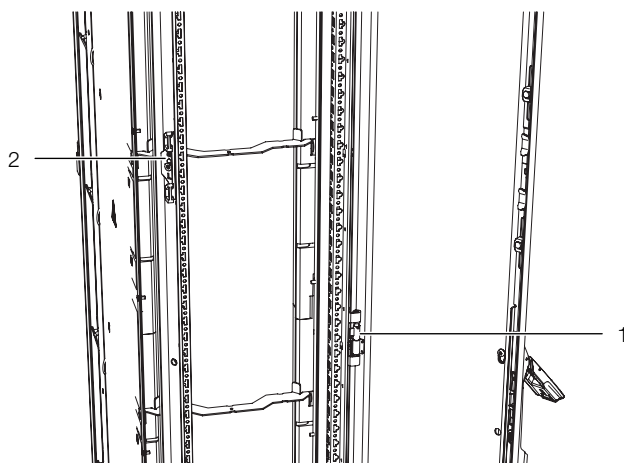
éléments de fixation sur le Liquid Cooling Package – vue de l'arrière
